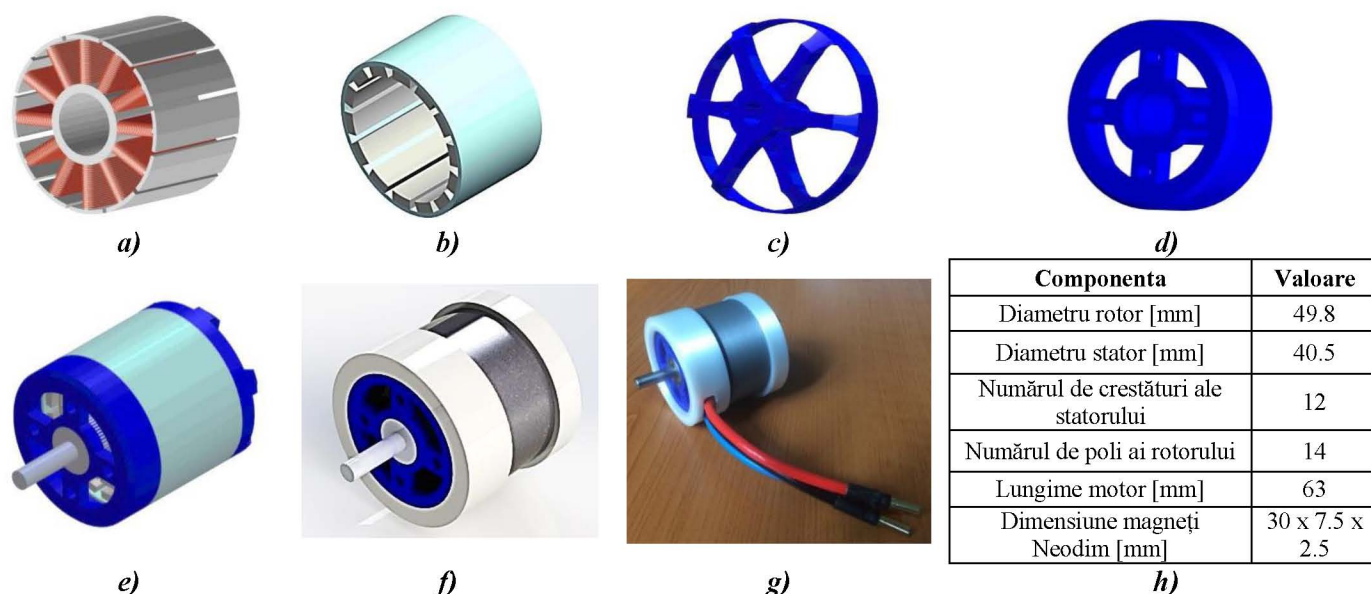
Modelarea CAD a motorului electric: a) statorul bobinat; b) rotorul prevăzut cu magneți; c) carcasă dreapta; d) carcasă stânga; e) modelul 3D a motorului; f) motorul cu elemente de rigidizare; g) motorul fabricat prin procedeul de extrudare termoplastică; h) caracteristicile motorului
